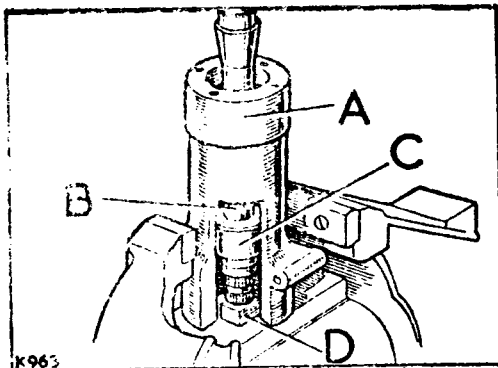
Caja compensadora, eje y taco de apoyo en su posición correcta.
